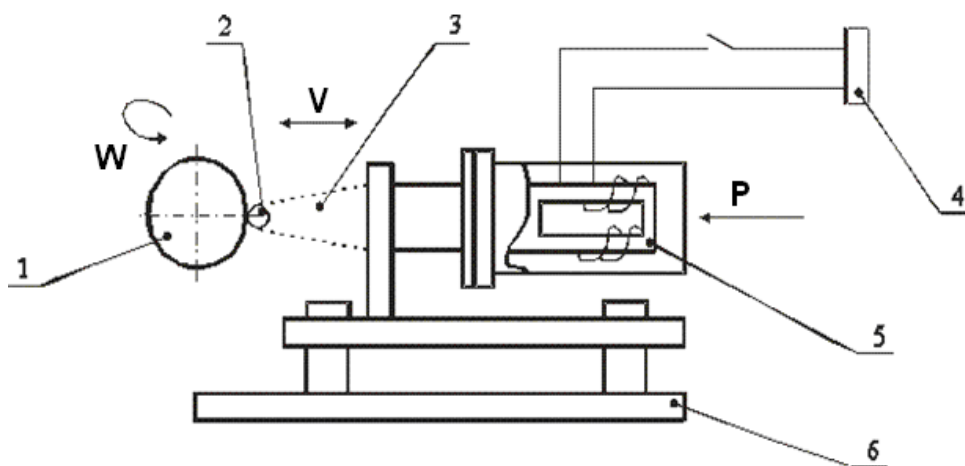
Схема размещения ультразвуковой системы на токарном станке: 1 – обрабатываемая деталь; 2 – индентор; 3 – концентратор; 4 – генератор; 5 – магнестрикционный преобразователь; 6 – суппорт станка
